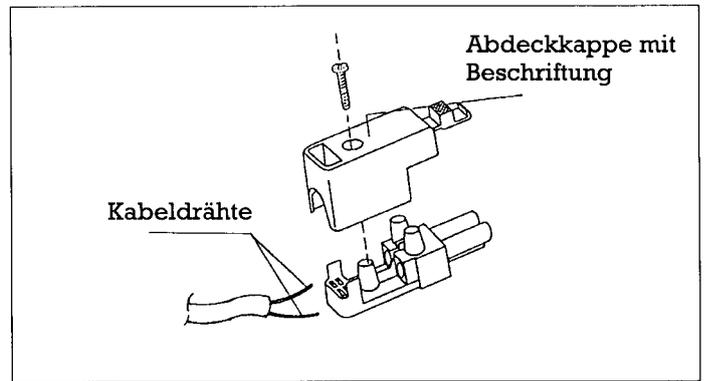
Steckerteil mit losgeschraubter Abdeckkappe
